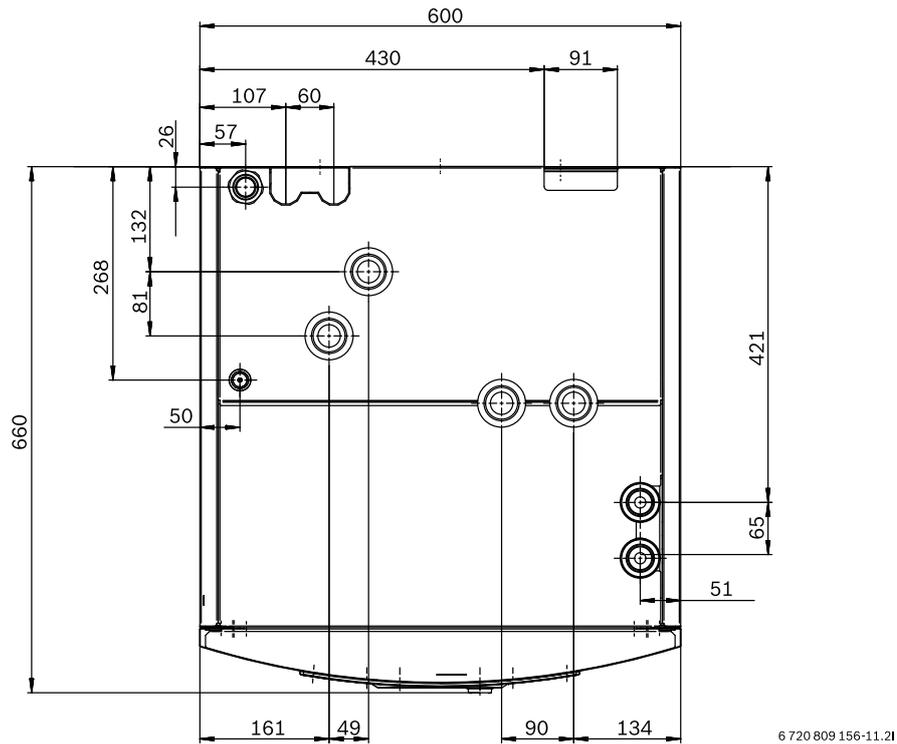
Distancias del módulo, vista en planta (medidas en mm)
